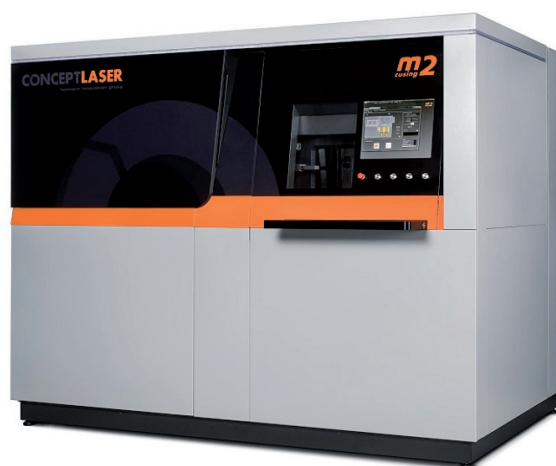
3D-принтер Concept Laser M2 Cusing для печати из металла (США)
